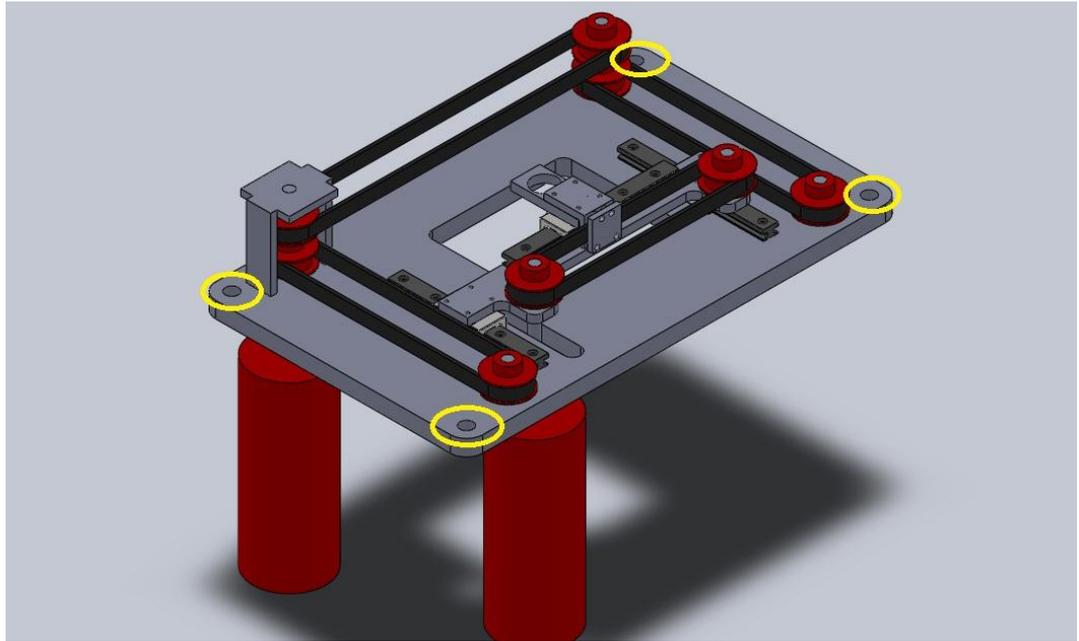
Pormenor para a fixação da estrutura á placa
